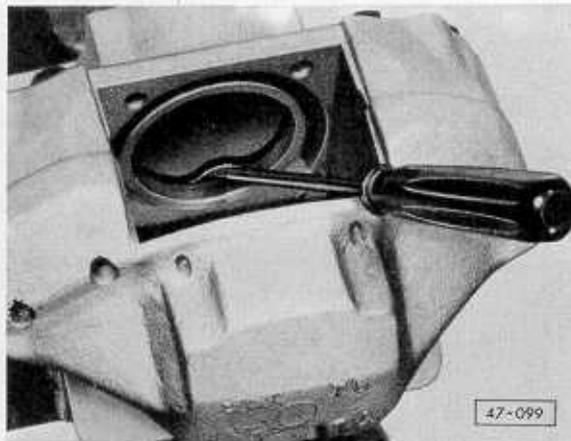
Dichtring vorsichtig mit einem Schraubenzieher ausbauen.
